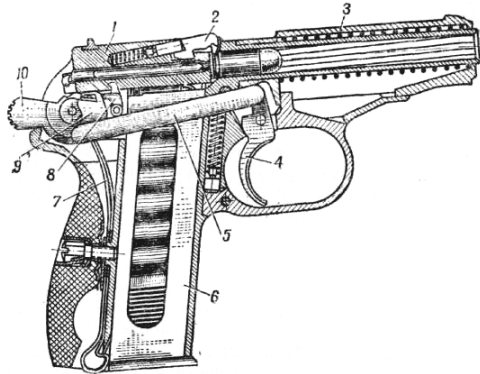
Положение частей и механизмов пистолета перед выстрелом: 1 – затвор; 2 – выбрасыватель; 3 – возвратная пружина; 4 – спусковой крючок; 5 – спусковая тяга; 6 – магазин; 7 – боевая пружина; 8 – шептало с пружиной; 9 – рычаг взвода; 10 – курок
